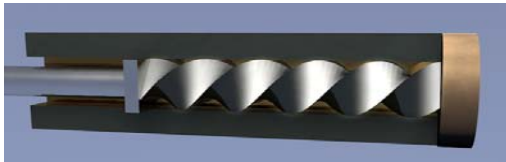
Установка заготовки в квадратный штамп с последующим прессованием
